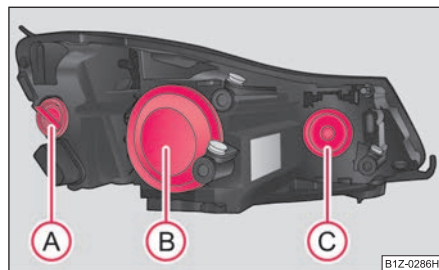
Faros delanteros: Posición de montaje de las bombillas
